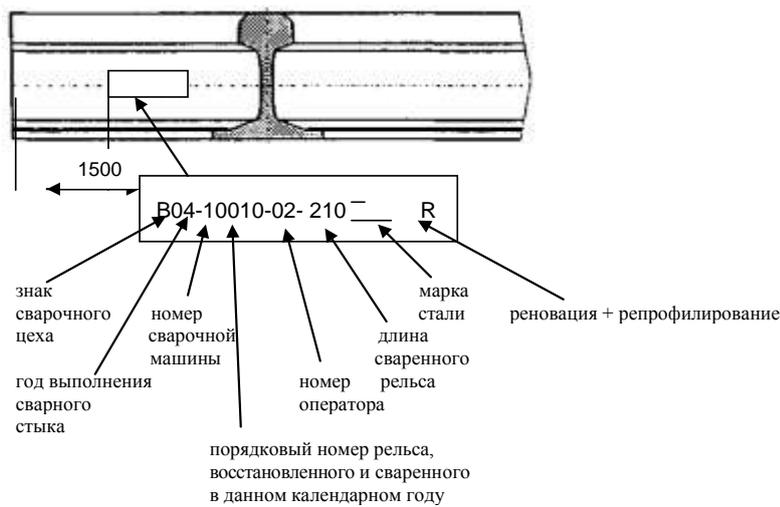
Маркировка рельса после реновации и сварки
